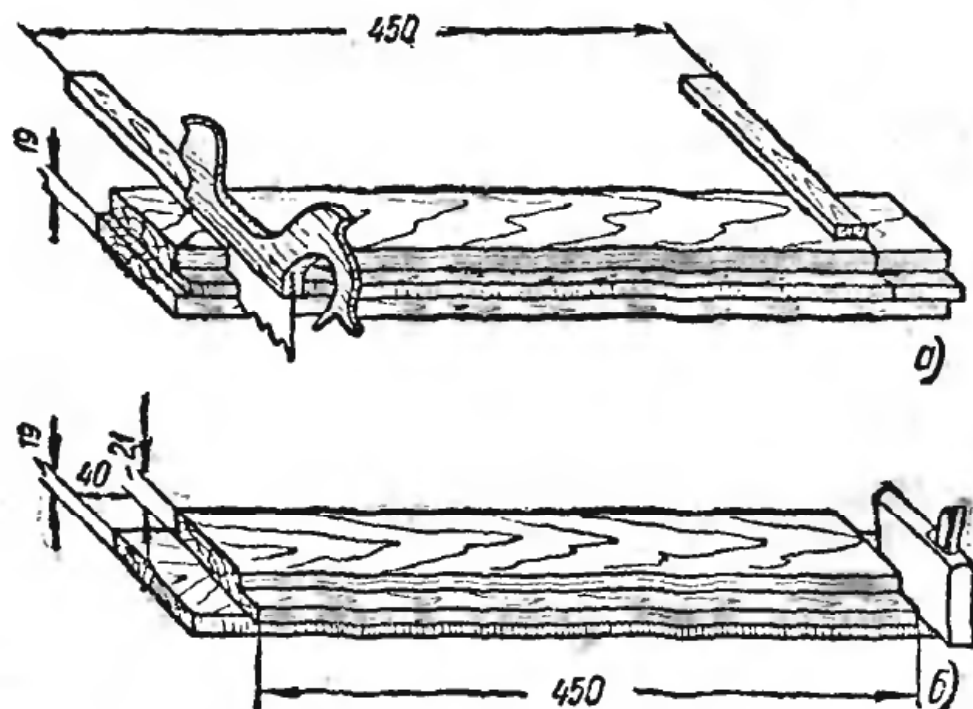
Разметка, зашлифовывание и отборка торцовых четвертей косолицем зензубелем: а — зашлифовывание размеченных торцовых четвертей на передней и задней стенках магазина; б — отборка зашлифованных торцовых четвертей.
